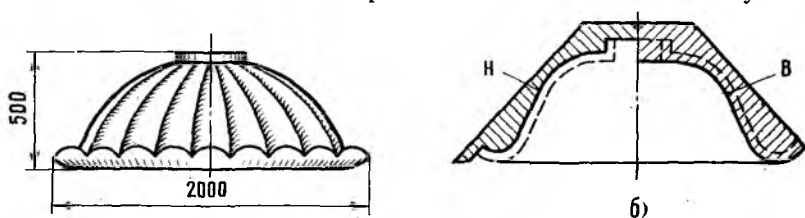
Фонтанная чаша и шаблоны для изготовления ее литейной формы
